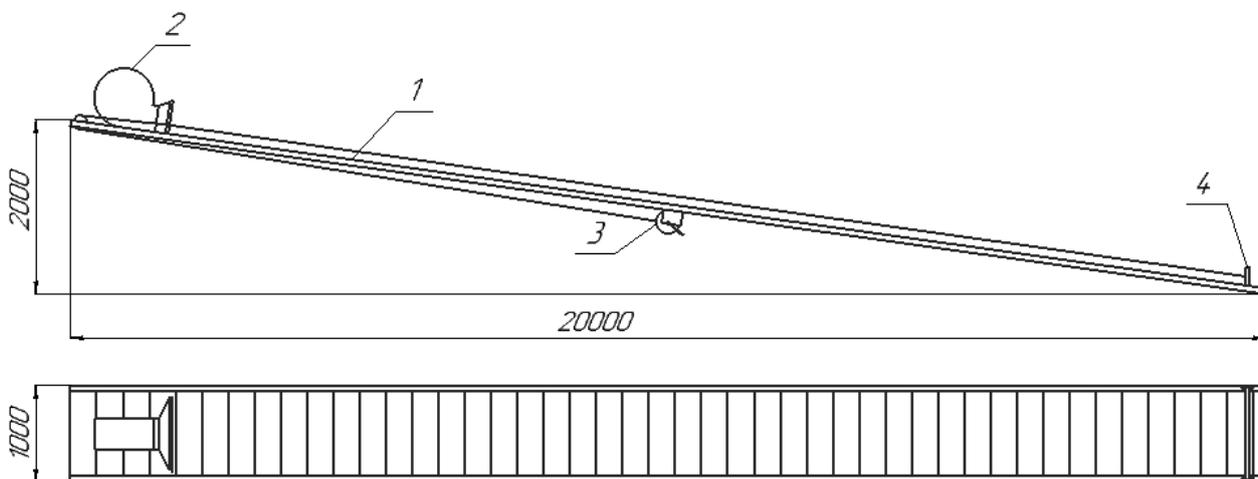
Рабочий чертеж установки для сушки пожарных рукавов:
